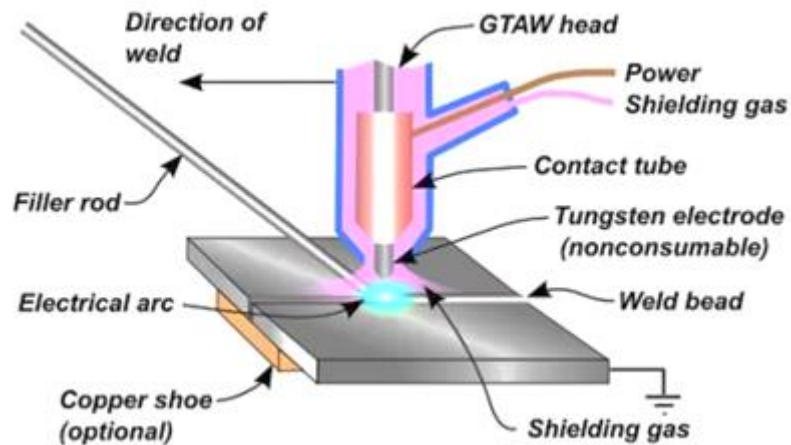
Sudare cu arc de tungsten cu gaz. Sursă: <https://www.weldingis.com/gtaw-welding/>
